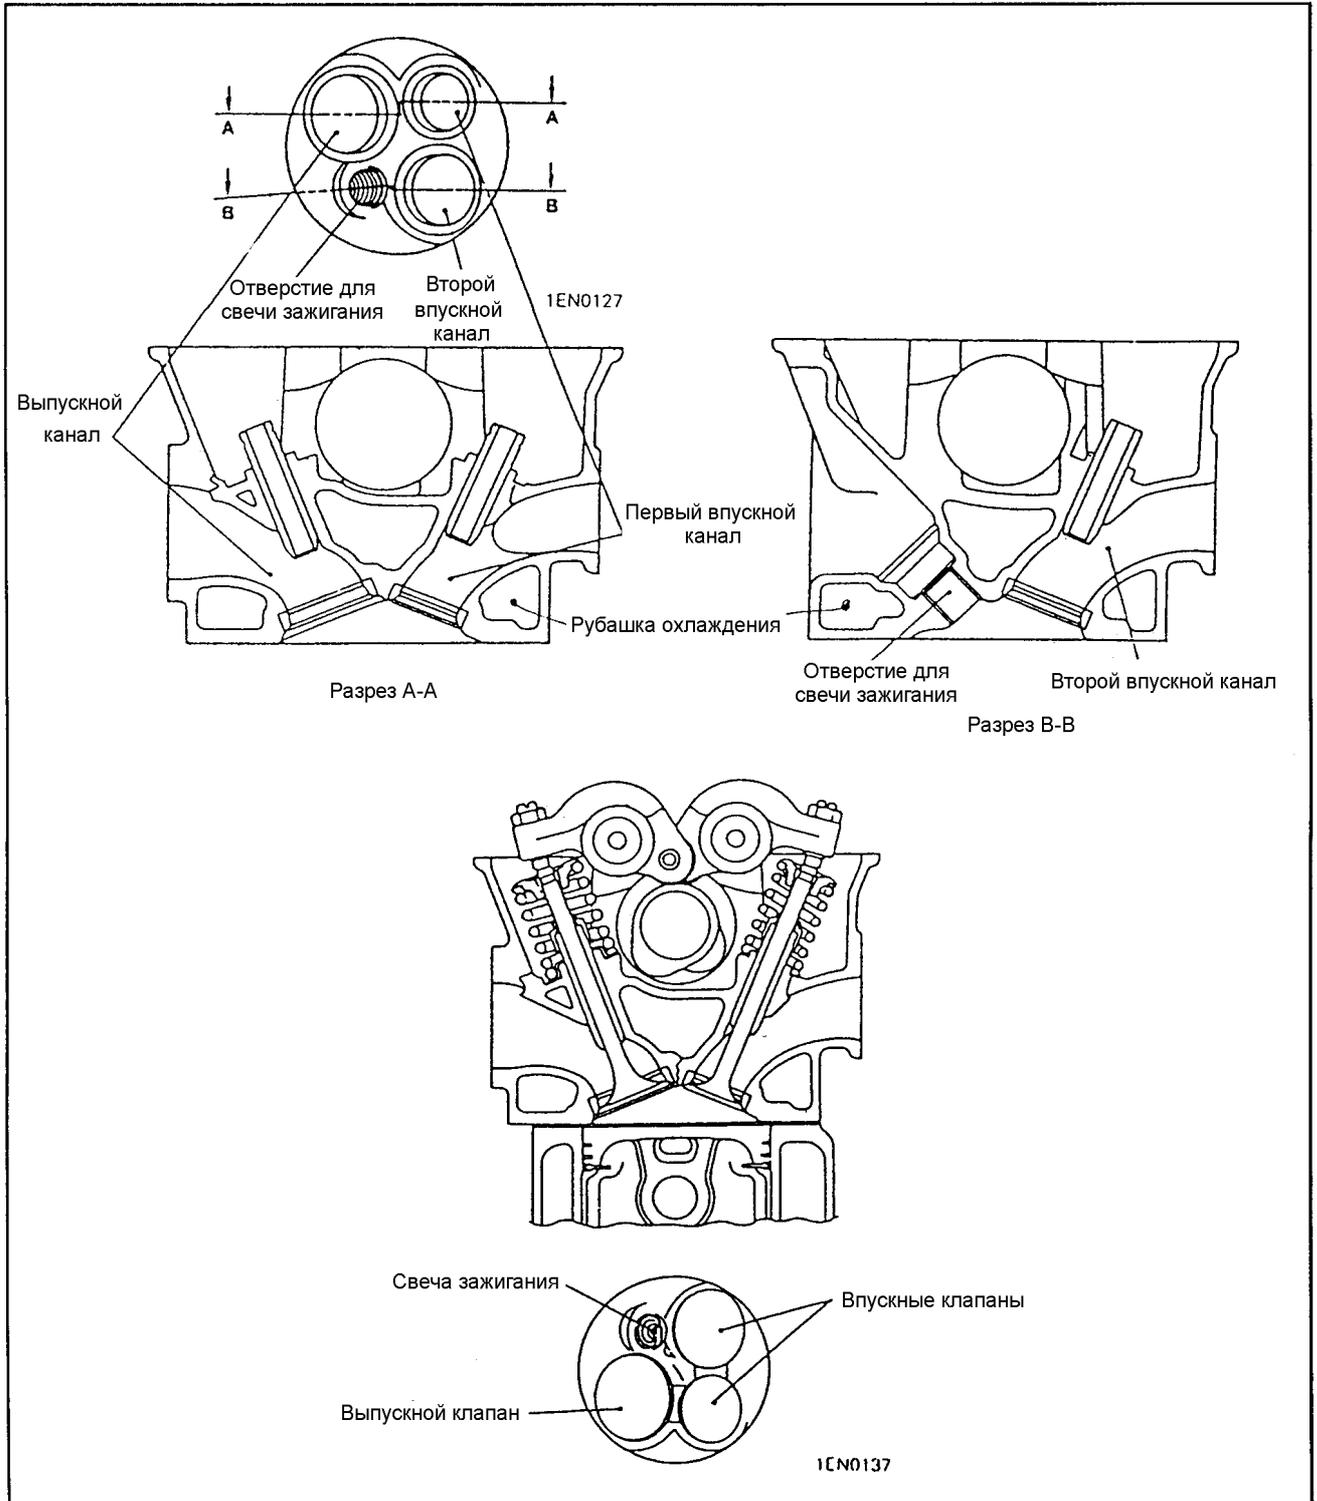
Головка блока цилиндров и клапанный механизм
